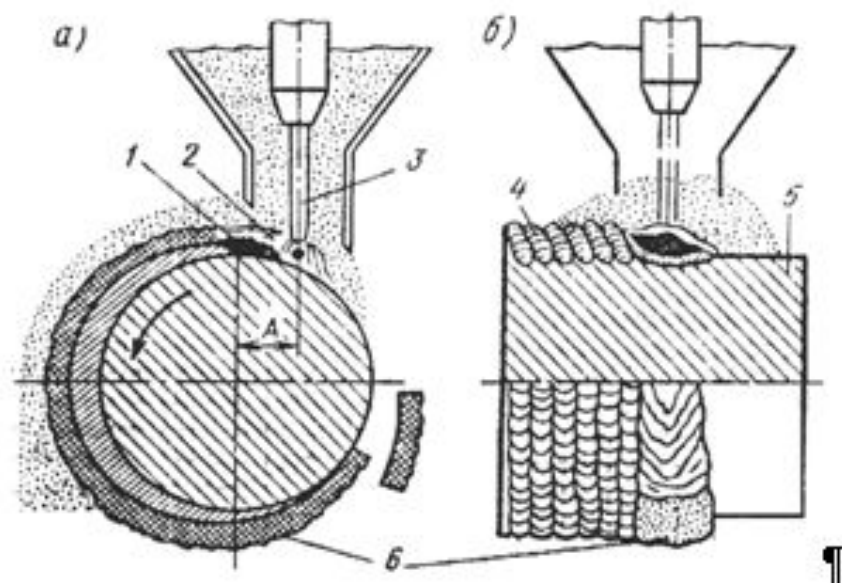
Схема наплавки под слоем флюса: а) — поперечный разрез; б) — продольный разрез; 1 — варочная ванна; 2 — расплавленный флюс; 3 — электродная проволока; 4 — наплавленный слой металла; 5 — деталь; 6 — шлаковая корка; А — смещение электродной проволоки с зенита. ¶
